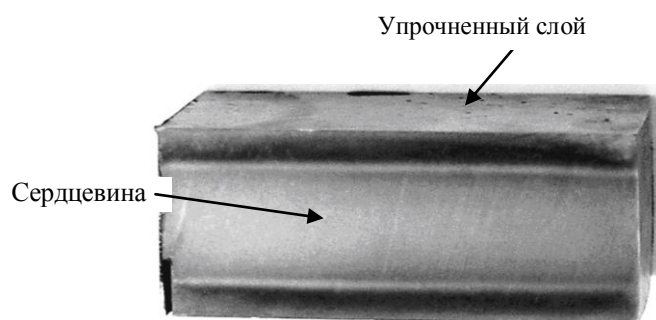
Схема расположения исследуемых поверхностей образца стали 60ПП
